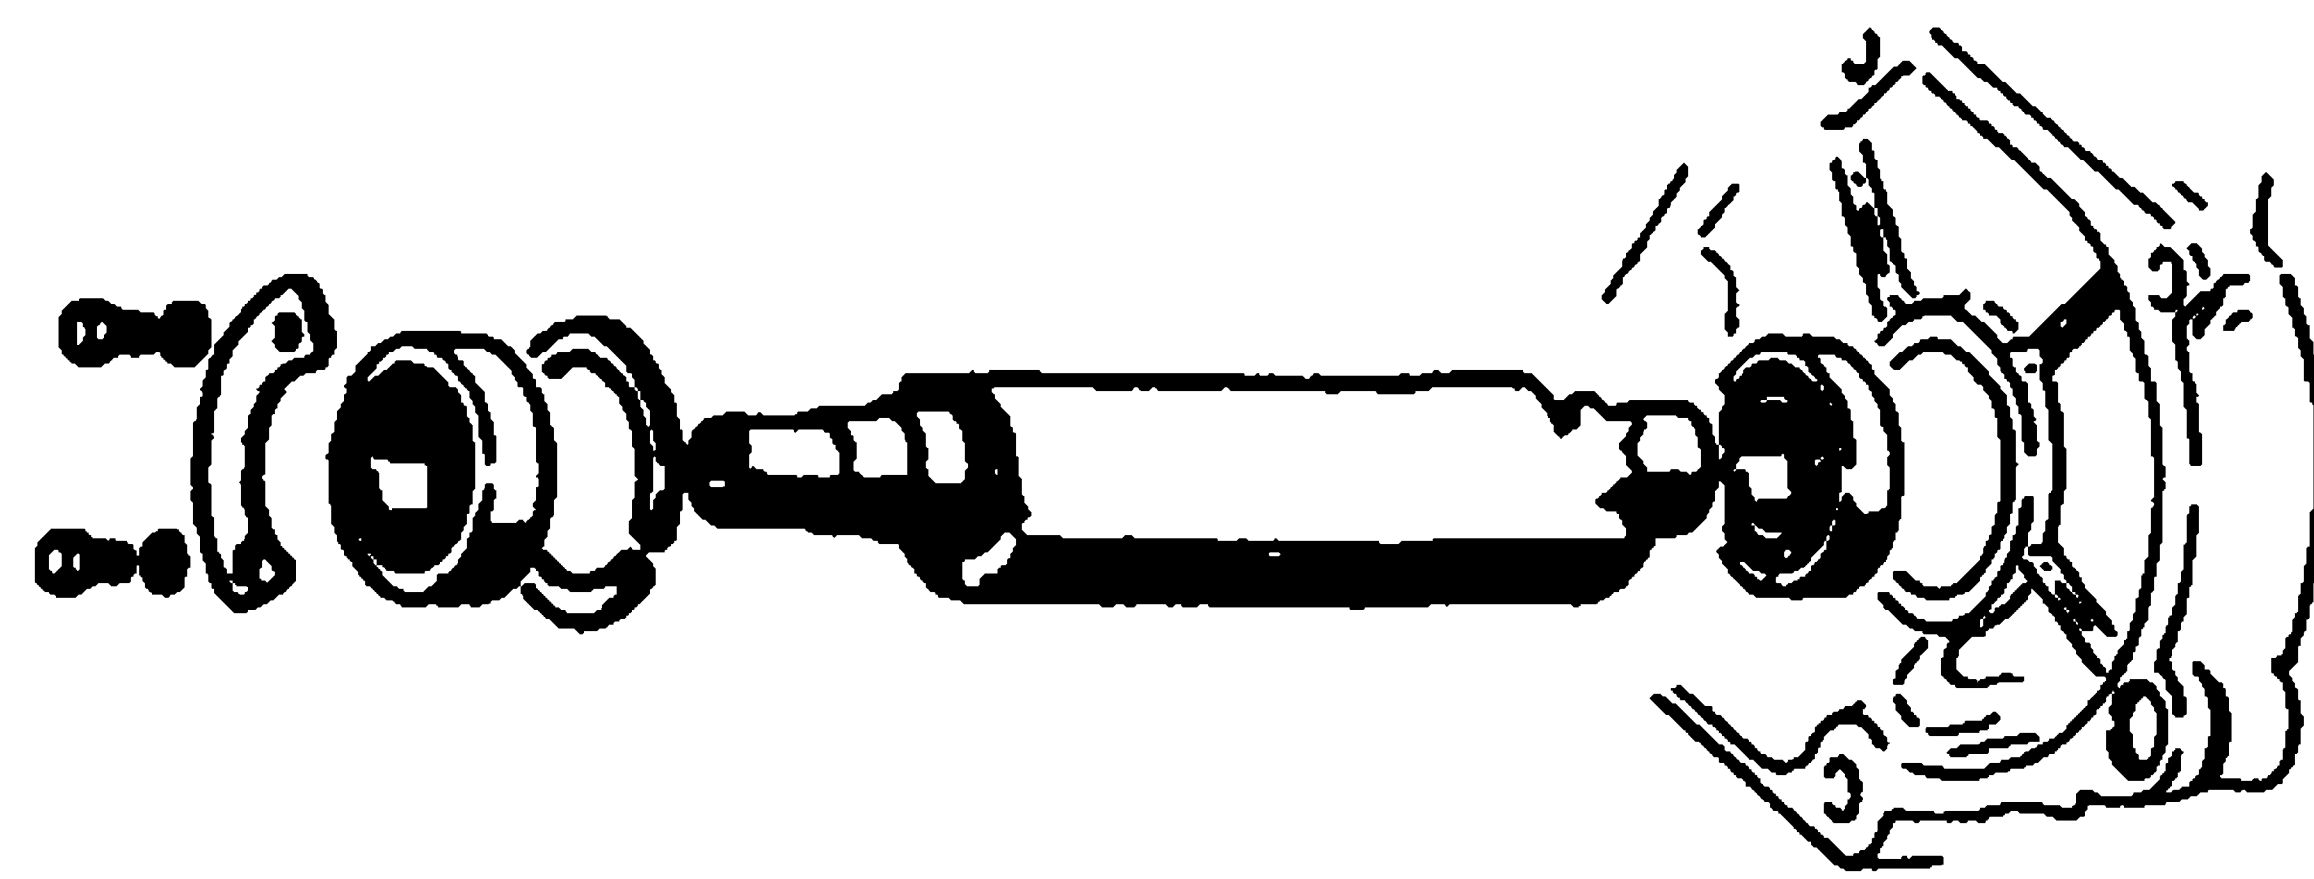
Уравнивающий вал двигателей 1111 и 11113
